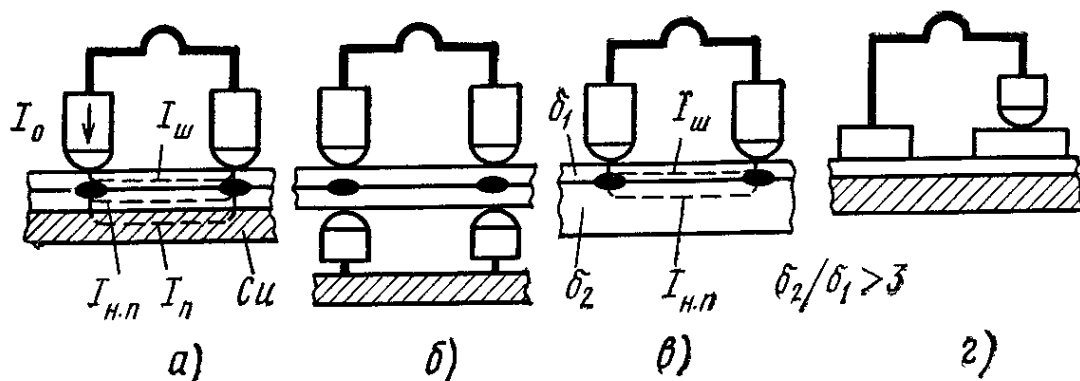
Схемы односторонней (а, в, г) сварки и сварки с замкнутыми нижними электродами (б)
